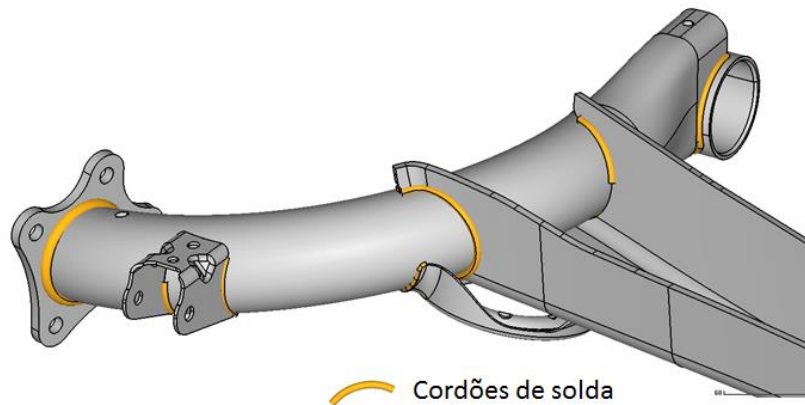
Detalhe dos cordões de solda do eixo de torção
